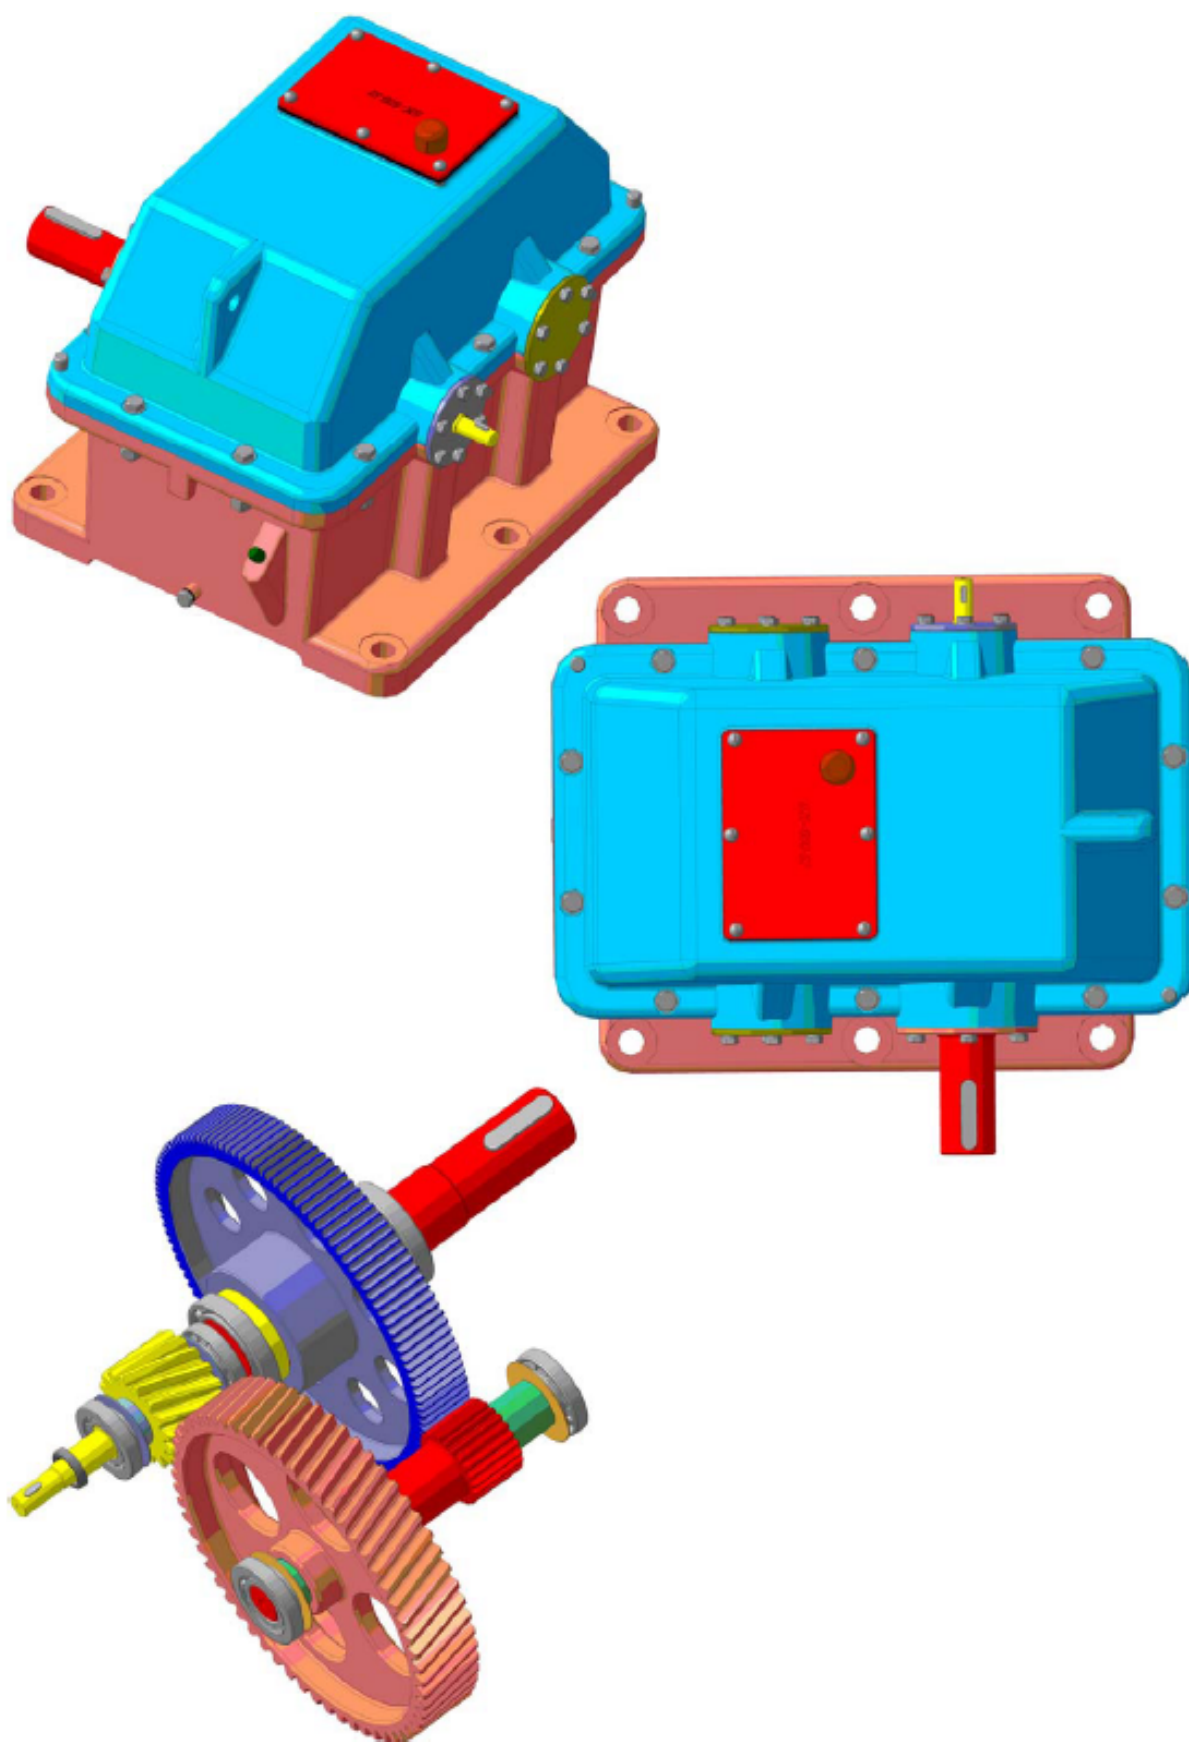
Циліндричний співвісний редуктор (Ц2С)
